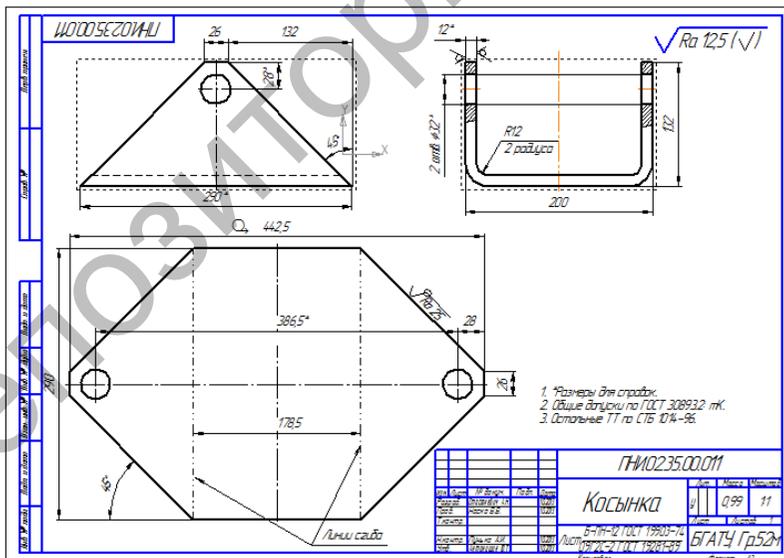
Чертеж косынки плуга ПНИ-2-35 с ее разверткой
